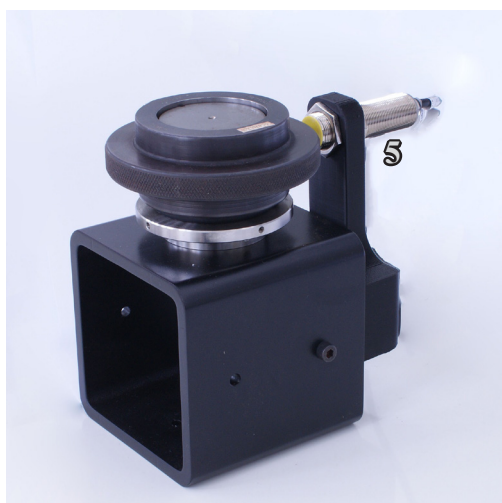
Detalhe do plug de medição e sensor indutivo IS101
